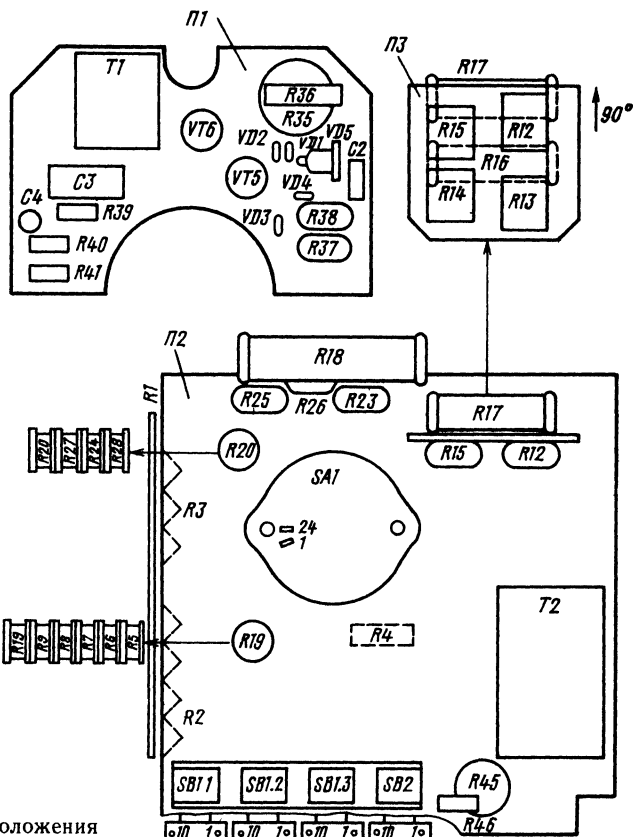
Схема расположения элементов на платах П1—П3, резисторных сборках и расположении секций и контактов переключателя SB1 прибора Ц4340
